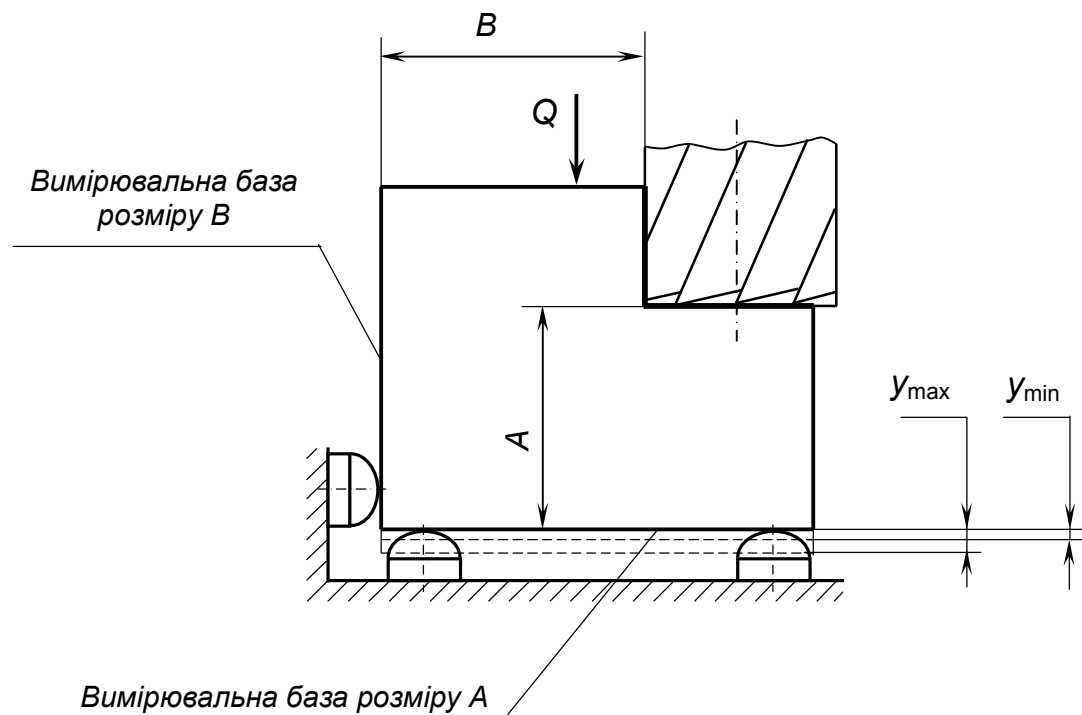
Схема, що пояснює механізм появи похибки закріплення
